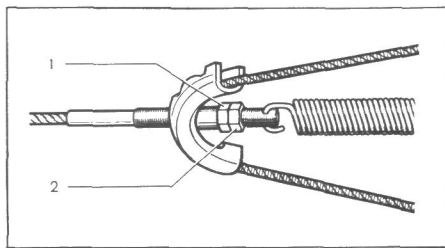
Регулировка хода рычага стояночного тормоза: 1 — регулировочная гайка; 2 — контргайка
